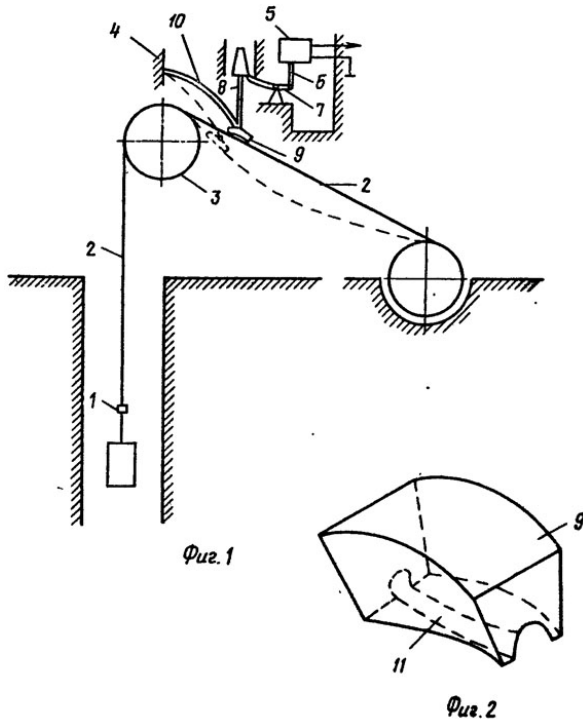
Устройство для защиты подъемной установки от напуска каната
